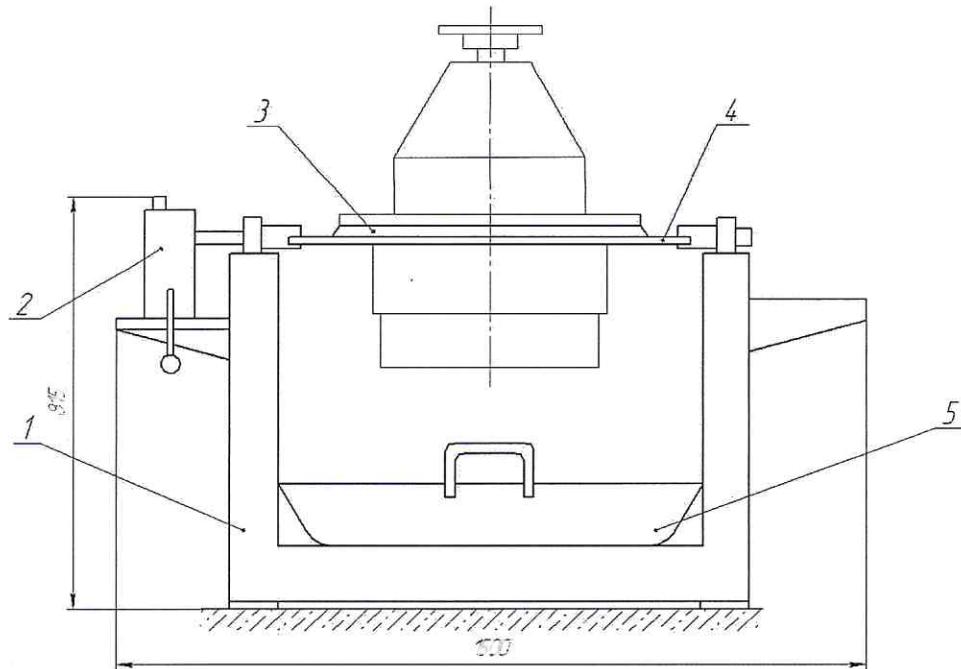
Схема стенда модели 24-15 для разборки и сборки редуктора заднего моста: 1-корпус; 2-механизм поворота; 3-съемная плита; 4-кантователь; 5-ванна.
